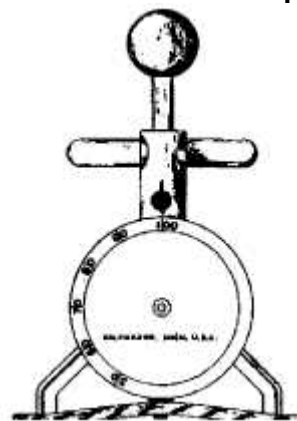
Измеритель Натяжения Ремня (Part No. 07-00203-00)
